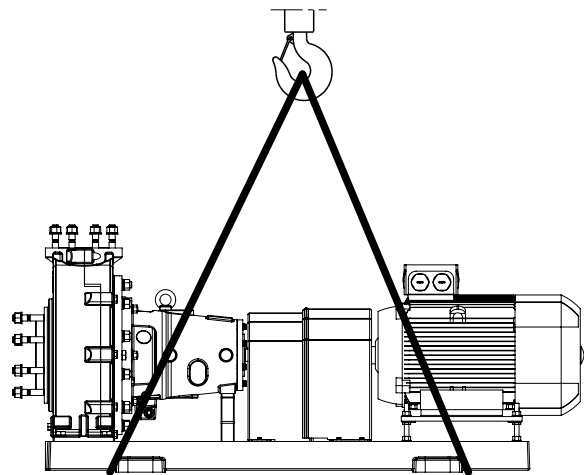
Hebezeug befestigen an Pumpenaggregat
